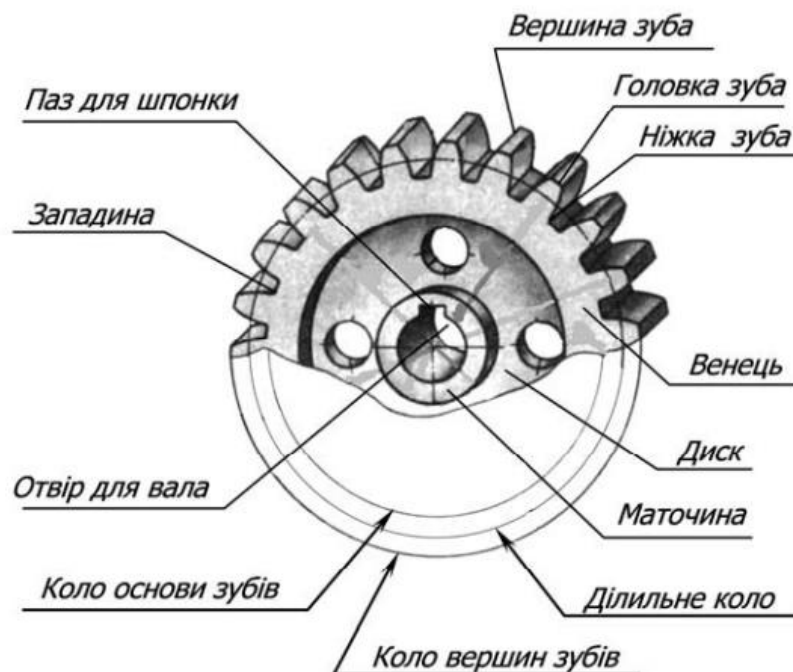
Загальний вигляд циліндричного зубчастого колеса
